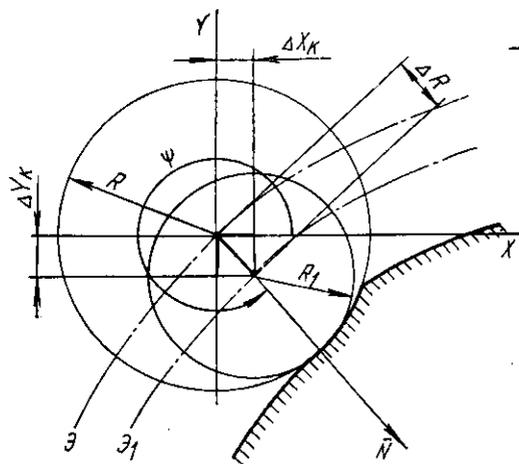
Схема фрезерования с коррекцией радиуса фрезы
